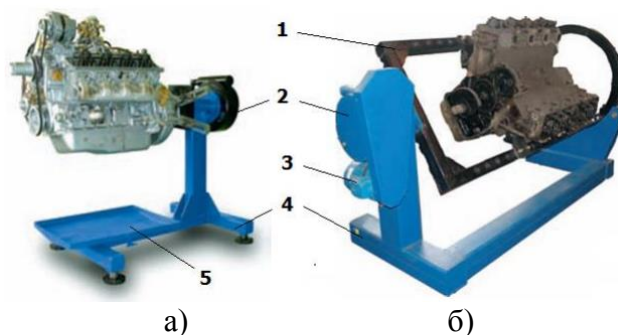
Стенд для ремонту агрегатів з консольною (а) та порталною (б) конструкцією рами: 1 – кронштейн-адаптер; 2 – черв'ячний редуктор; 3 – електродвигун; 4 – рама; 5 – піддон для збору рідини [2, с. 102-103]
